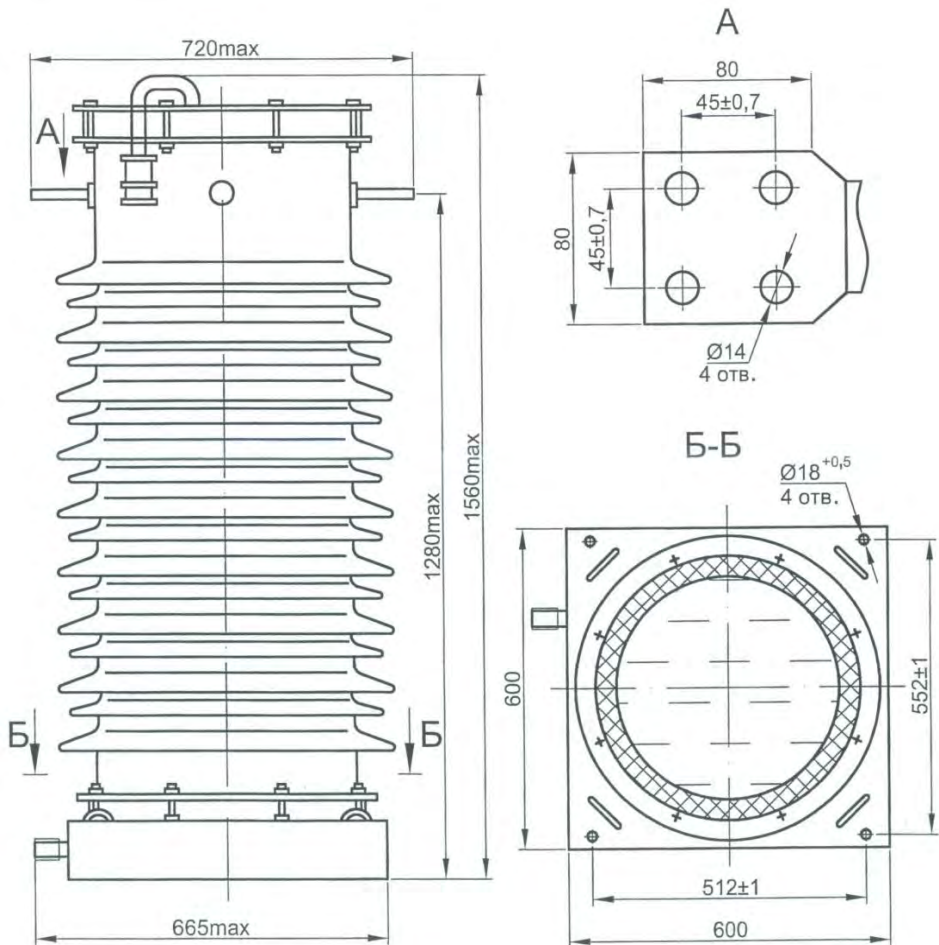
Общий вид трансформатора тока ТФЗМ 110
